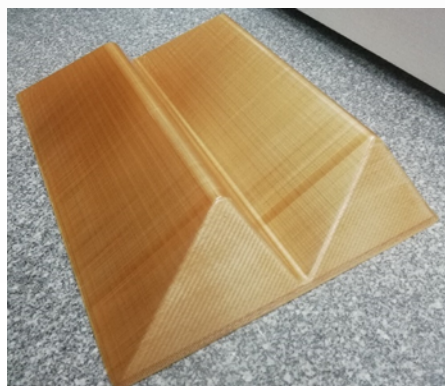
Moule PEI imprimé 3D pour le moulage par infusion sous vide d'une pièce avec une section en Z.
